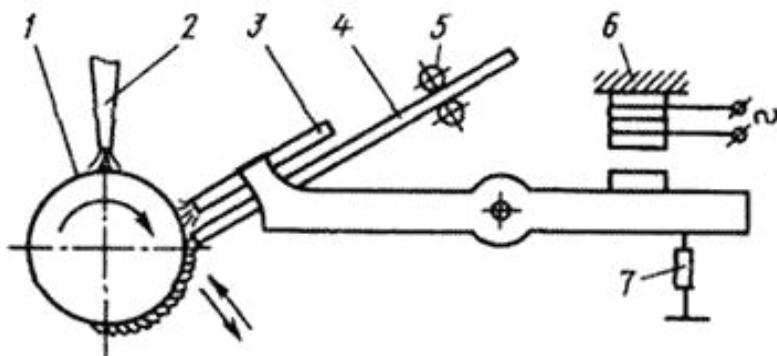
Схема вибродуговой наплавки: 1 — наплавляемое изделие; 2 — сопло для подачи охлаждающей изделие жидкости; 3 — сопло для подачи жидкости в зону сварки; 4 — электродная проволока; 5 — подающие ролики; 6 — электромагнитный вибратор; 7 — пружина
